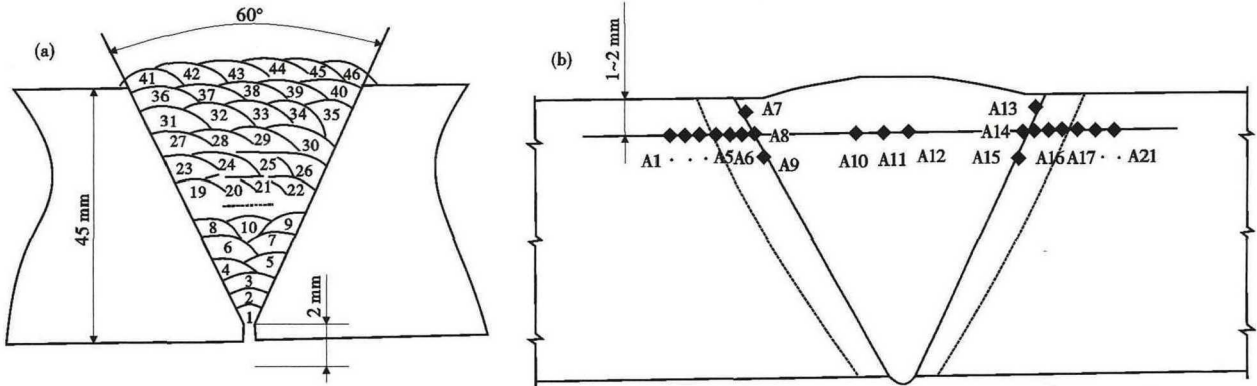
焊接道次(a)和对接头硬度试验点位置(b)示意图
